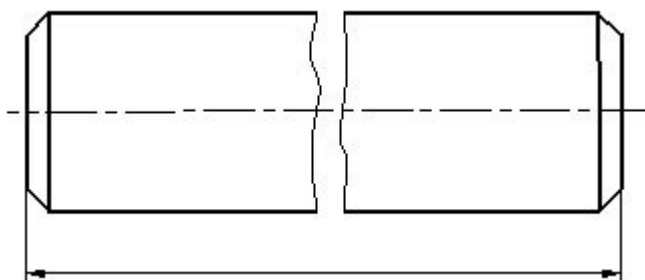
Пример обозначение размера при изображении детали с разрывом
